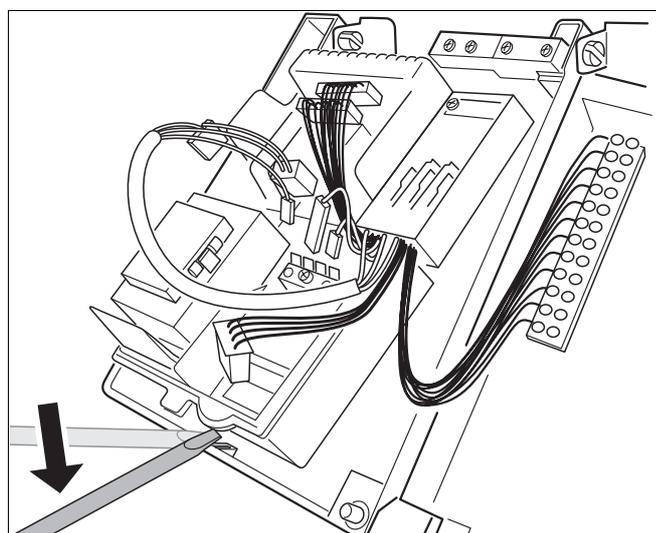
Sollevare leggermente l'UBA ed estrarlo
